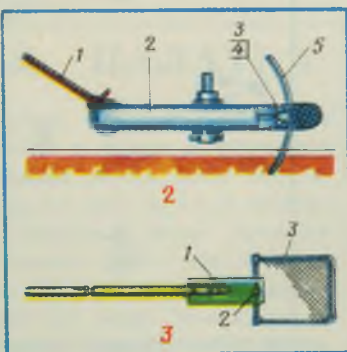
Крепление якоря к колесу: 1 — якорный канат; 2 — колесо; 3, 4 — болт М10 с гайкой-барашком; 5 — якорь.
